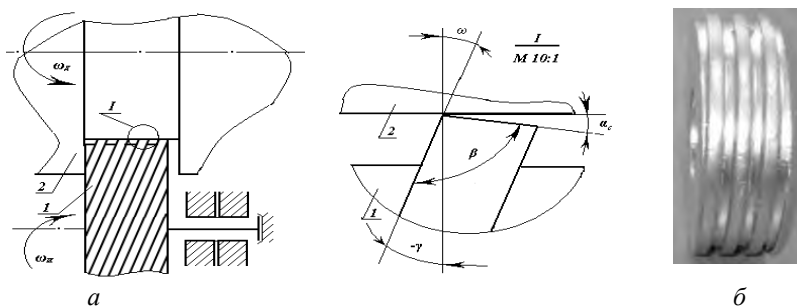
Принцип работы многозевыного винтового ротационного резца: схема (а) и фото (б) для опорных участков деталей повышенной точности: 1- режущие элементы. 2 - обрабатываемая деталь. ω_d — угловая скорость детали; ω_n - угловая скорость режущих элементов; ω - угол подъёма по винтовой линии; α_c - статический задний угол режущего элемента; γ_k - статический передний угол режущего элемента; β - угол клина
